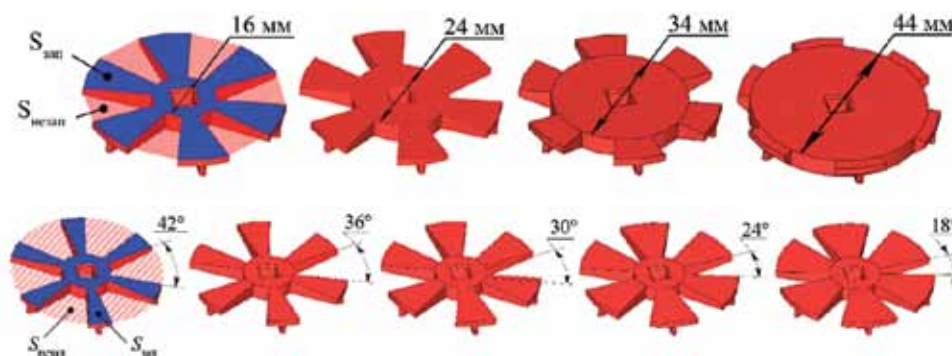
Формы разбрызгивателей с различными значениями внутреннего диаметра разбрызгивателя (a) и углового шага лопастей (b)
